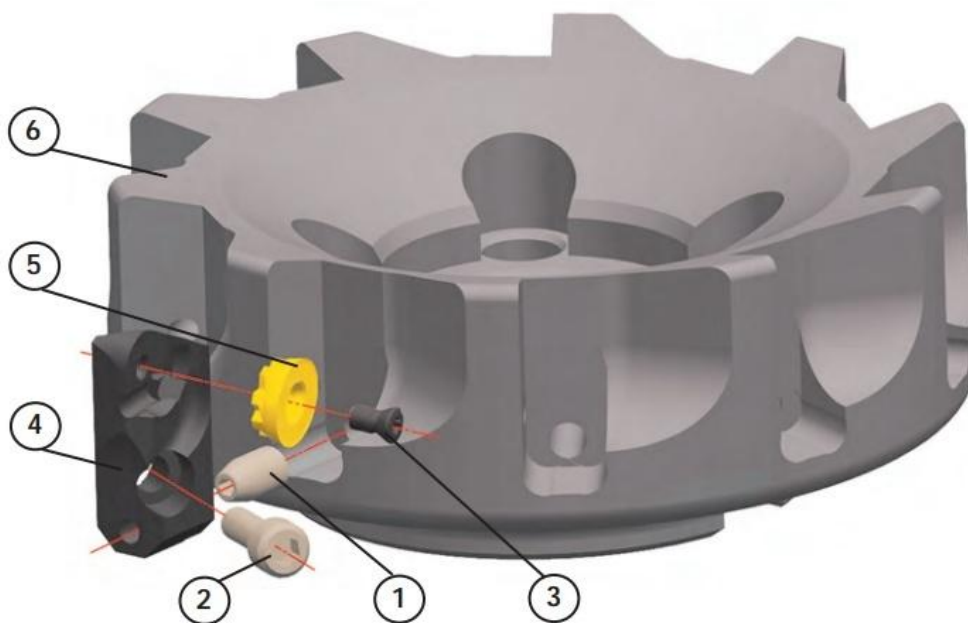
Конструкция фрез компании СКИФ-М:
